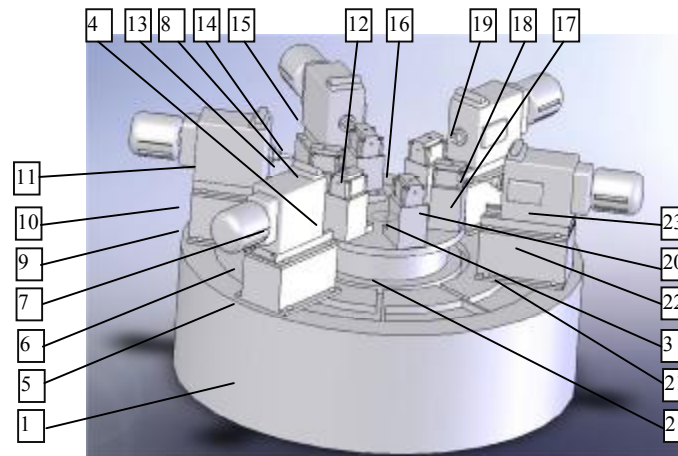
Агрегатний верстат з п'ятьма робочими позиціями.
